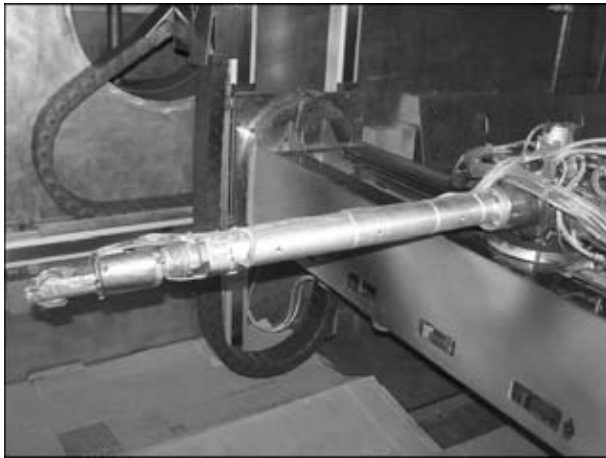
90°-Поворотная система для ремонта и косметического заглаживания обратного валика шва
